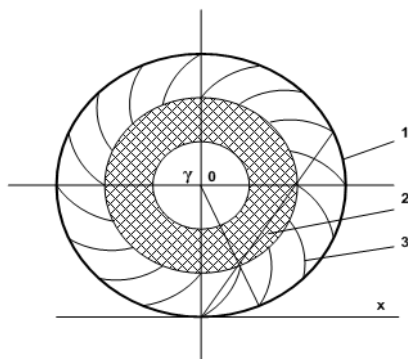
Конструкция пьезоэлектрической машины нереверсивного двигателя типа ПД: 1 -стальной стакан (ротор); 2 -статорный пьезоэлемент; 3 -упругие стальные пластинки (толкатели).
